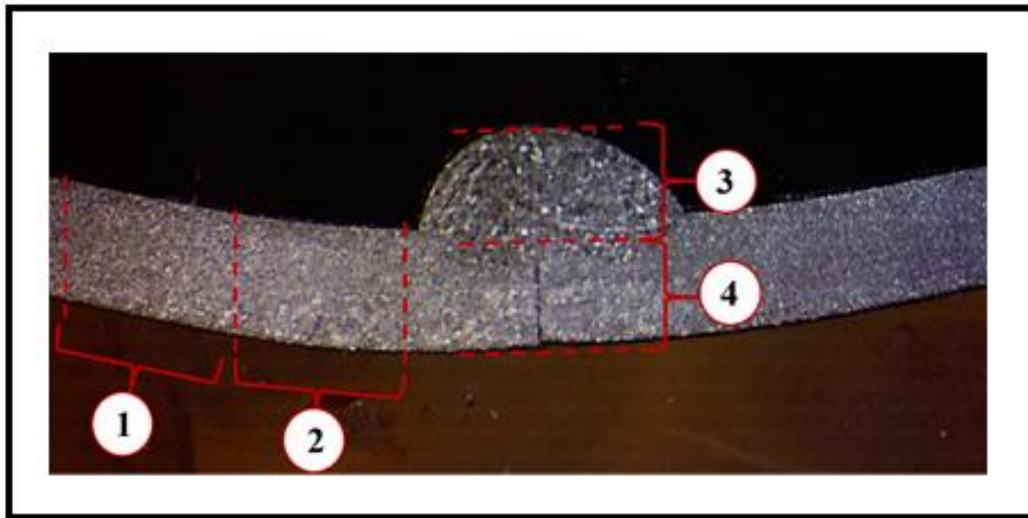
Photographie d'un soudage semblable 304L/304L.
